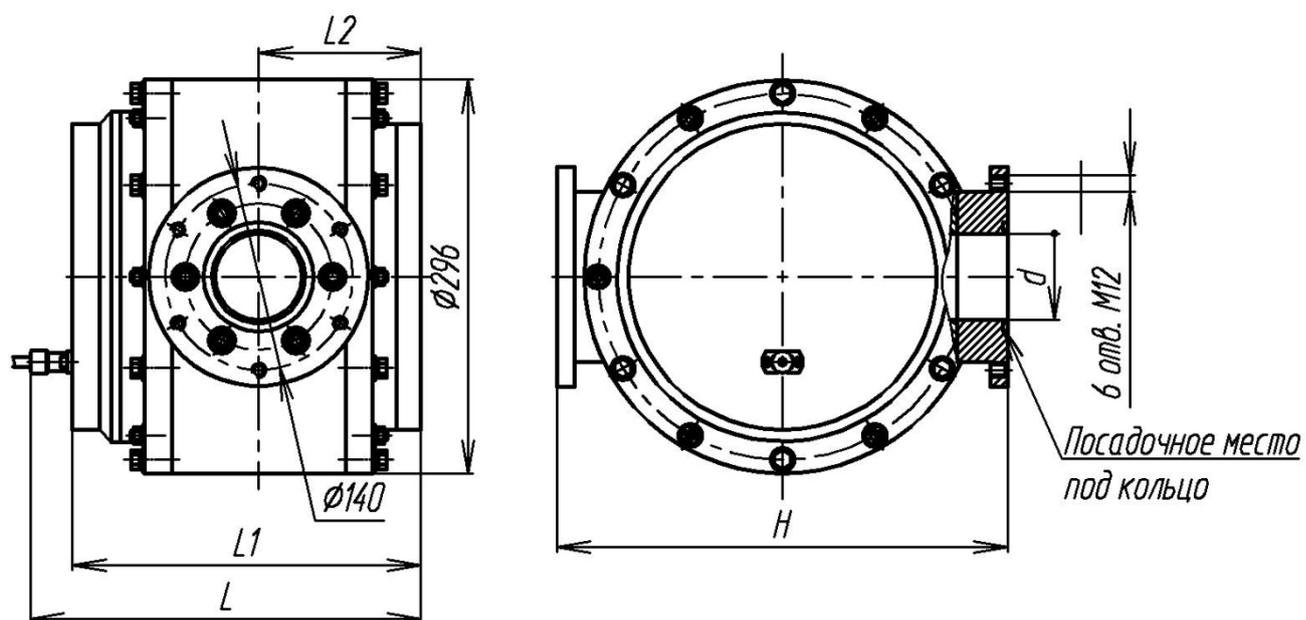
Габаритные и присоединительные размеры типа РВШ-РЛ
